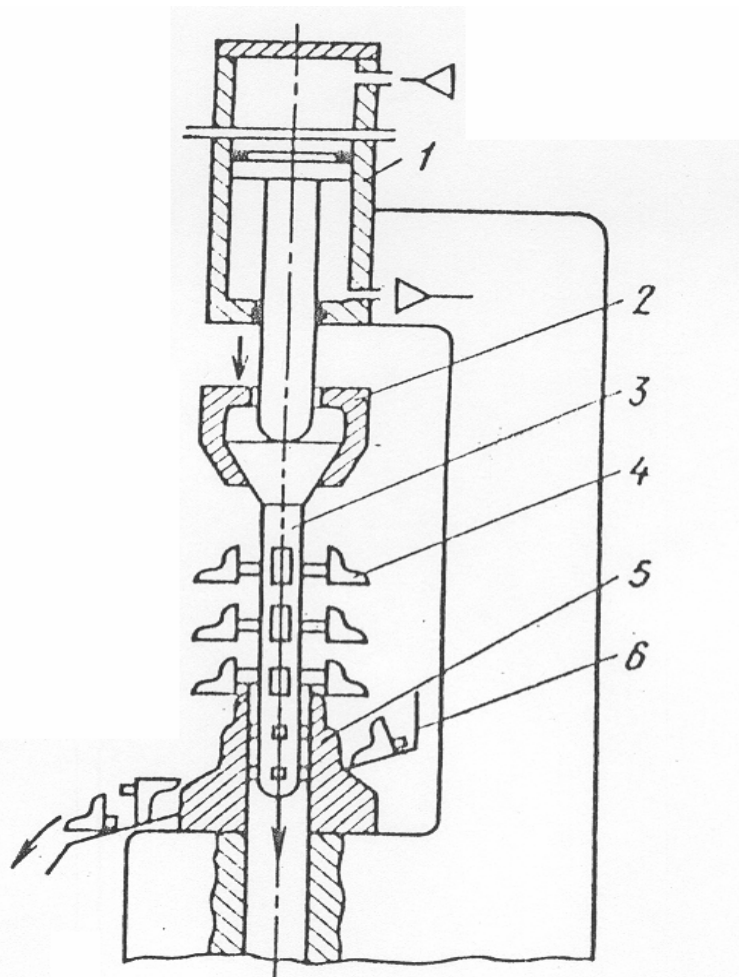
Схема устройства пресса для отделения отливок от стояка: 1 – гидроцилиндр; 2 – зажим; 3 – блок отливок; 4 – отливки; 5 – штамп; 6 – лоток.
